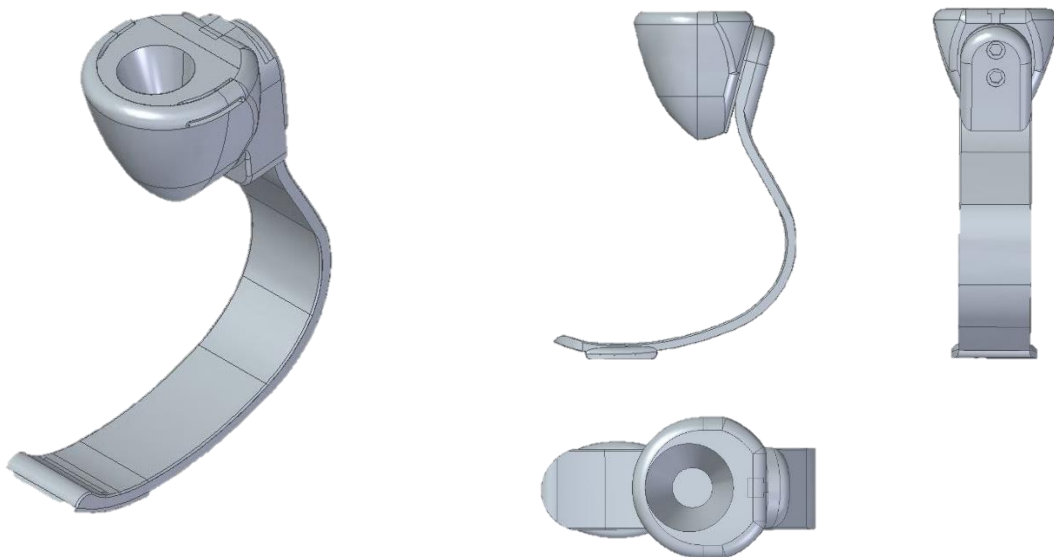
Vista isométrica del diseño 3D junto al alzado, planta y perfil.
